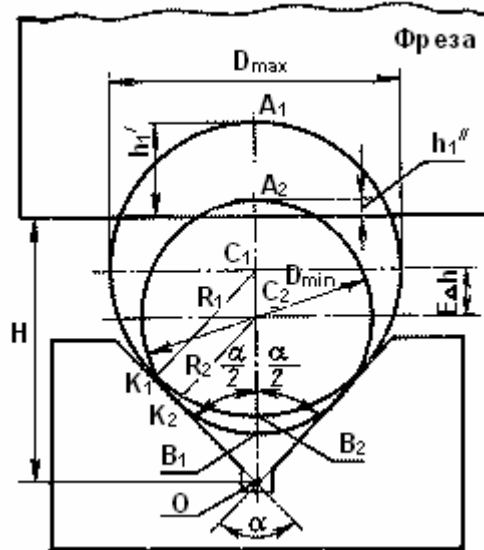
Схема для визначення похибок базування при установленні вала на призму
